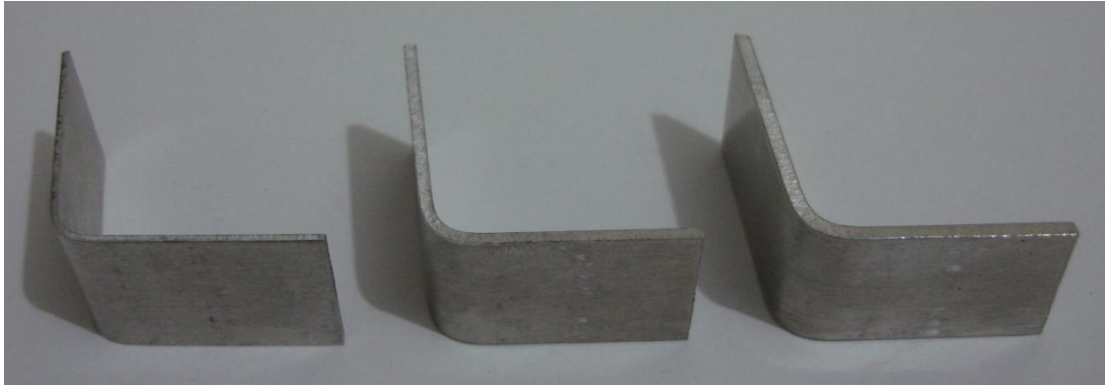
1-1,5 ve 2 mm kalınlığındaki AL 5754 sac malzemelerin, 120° açılı ve 1 mm uç kavisli zımba ile bükülmesi sonu elde edilen numuneler
